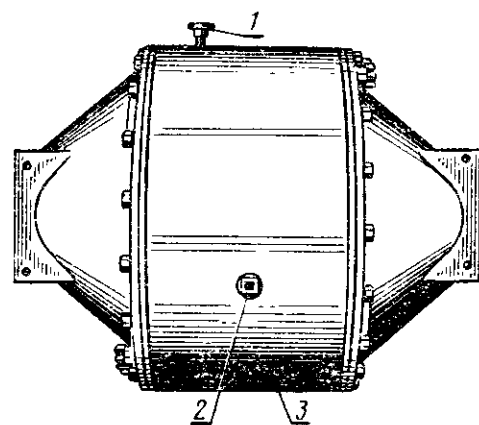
Главная передача: 1 — сапун; 2 — пробка контрольного отверстия; 3 — пробка сливного отверстия.
